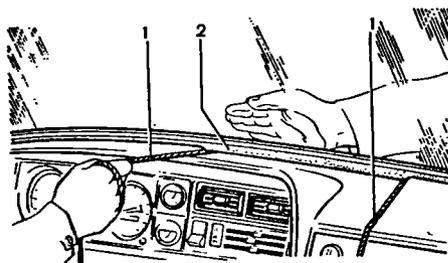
Установка ветрового стекла: 1 - шнур для установки ветрового стекла; 2 - уплотнитель
